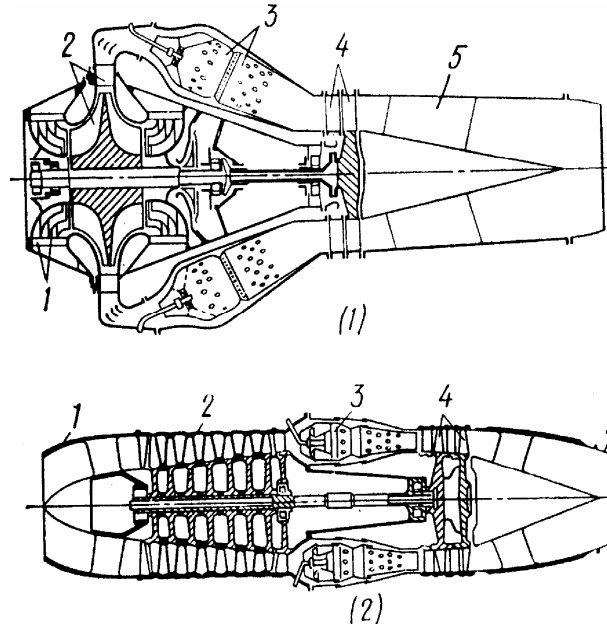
Турбокомпрессорные воздушно-реактивные двигатели: а – принципиальные схемы: (1) – с центробежным компрессором: 1 – входное устройство компрессора, 2 – центробежный компрессор, 3 – камеры сгорания, 4 – турбина, 5 – выходное сопло; (2) – с осевым компрессором: 1 – входное устройство компрессора, 2 – осевой компрессор, 3 – камеры сгорания, 4 – двухступенчатая турбина, 5 – выходное сопло
